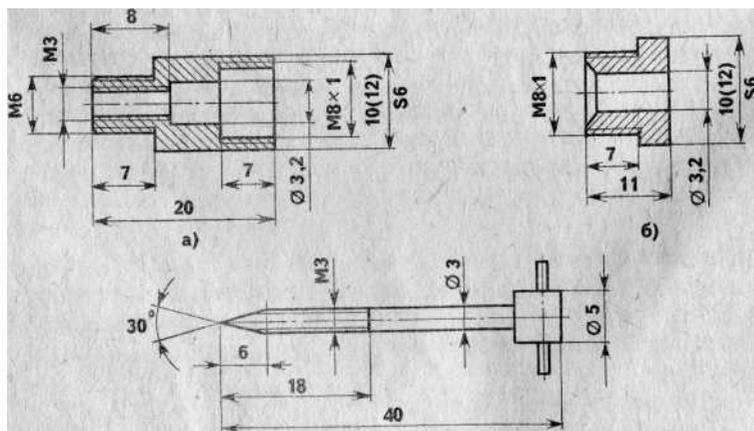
Детали устройства для регулирования подачи топлива в отопитель: а) корпус; б) гайка уплотнения; в) игла.
